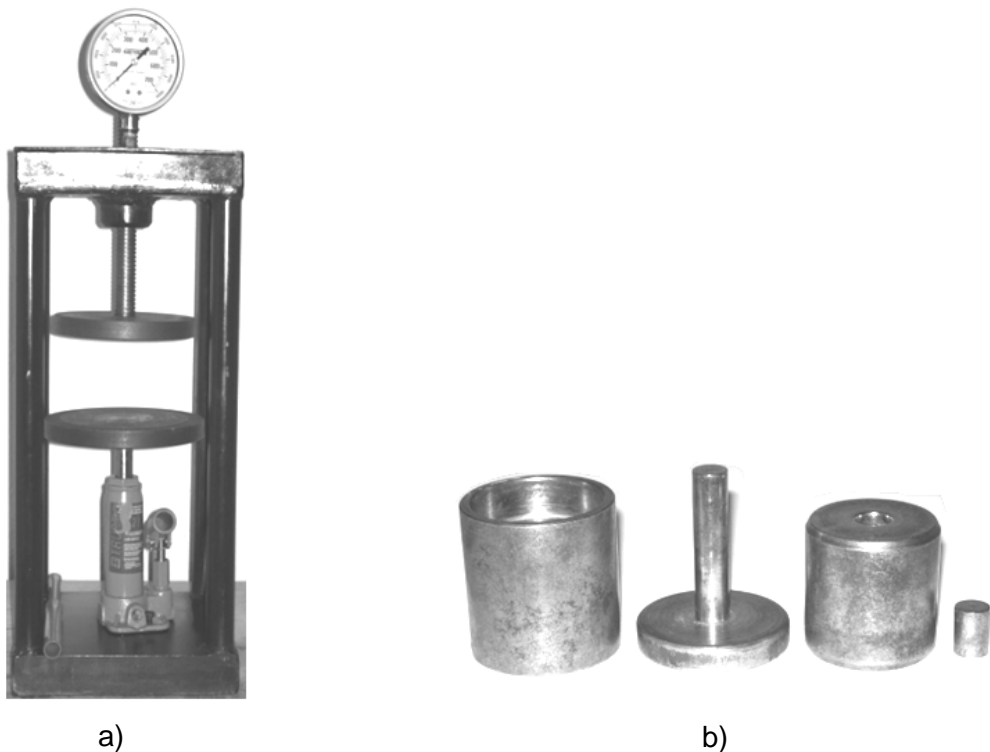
Equipo para conformado: a) prensa uniaxial y b) molde.
